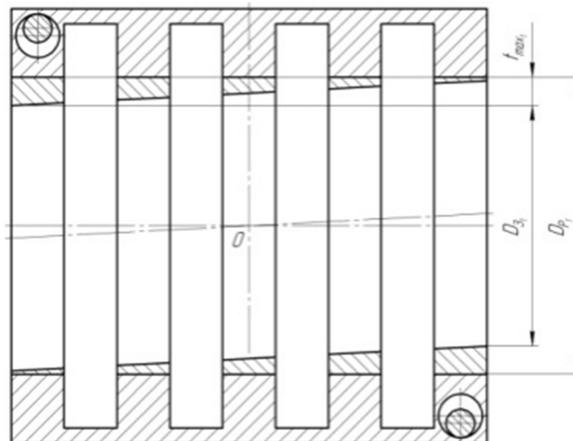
Схема образования неравномерности припусков в ГПО:
